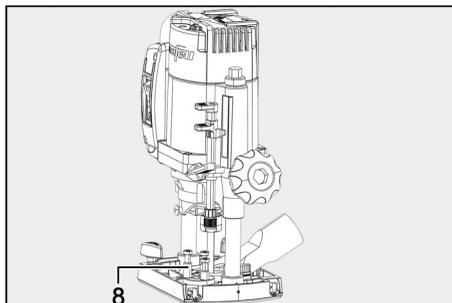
Ajustar las profundidades de fresado fijas mediante el tope de revólver.
